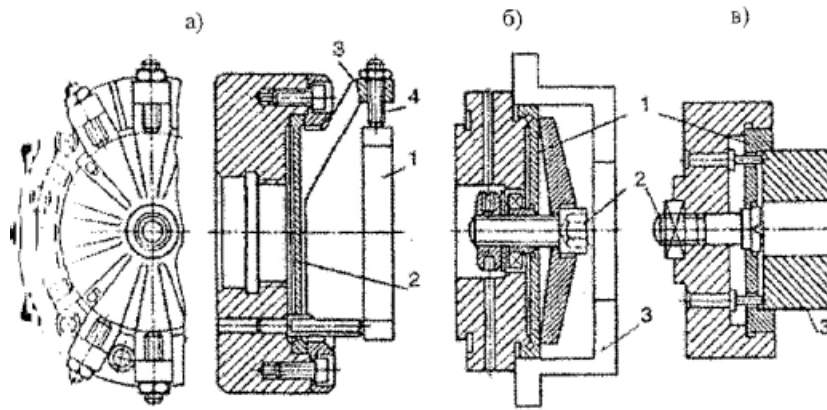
Конструкции мембранных патронов: а – рожкового типа (1 – заготовка; 2 – упругая мембрана; 3 – рожки; 4 – винт); б и в – чашечного типа (1 – упругая мембрана; 2 – винт; 3 – заготовка).
